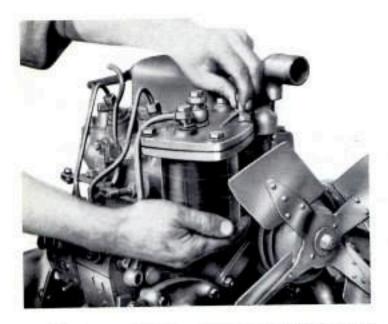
Smontaggio del motore: viene asportato il filtro gasolio.
